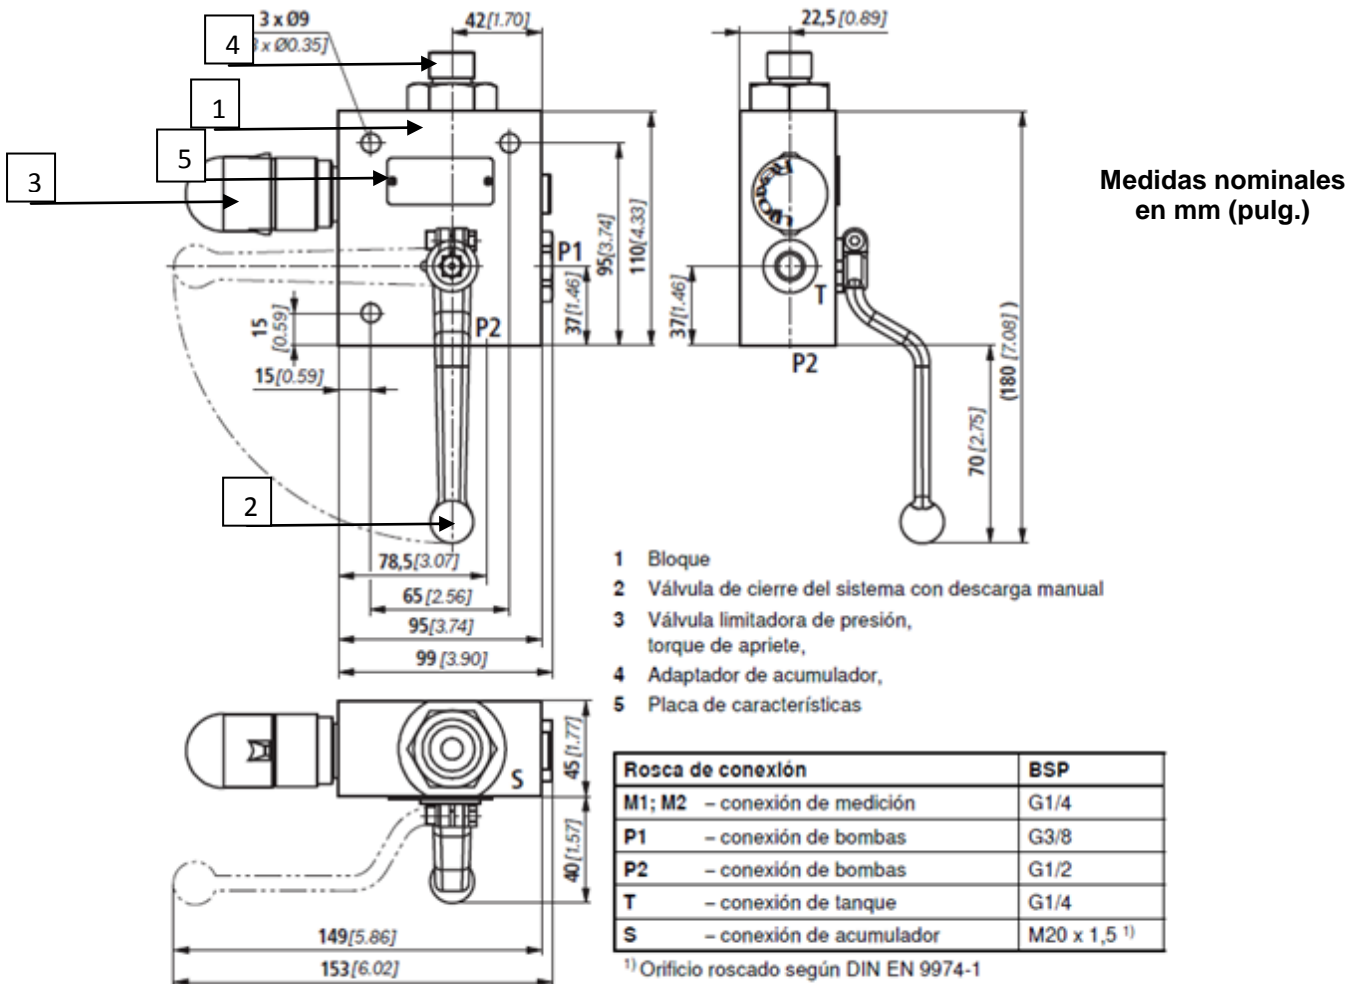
Dimensiones del bloque de cierre del acumulador
